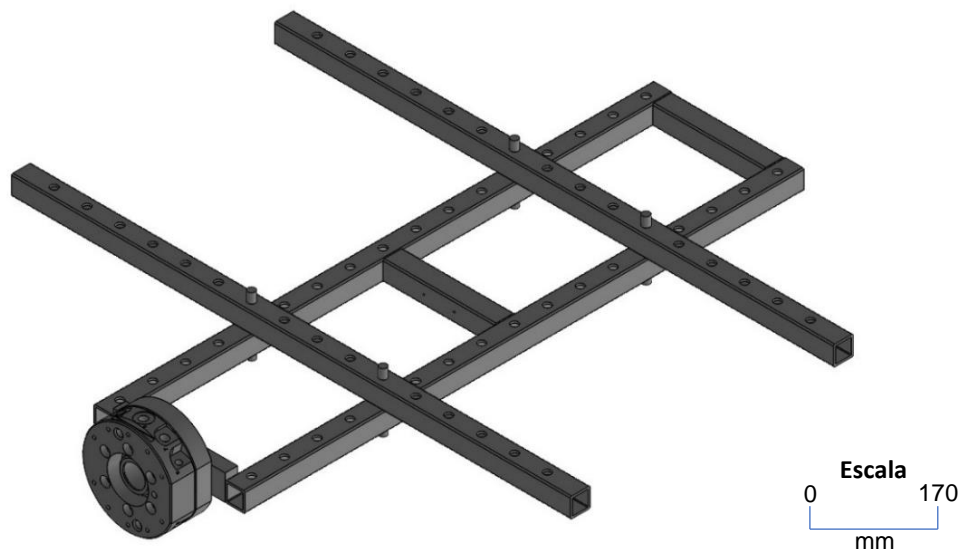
Assmbly completo dos componentes principais do frame.
